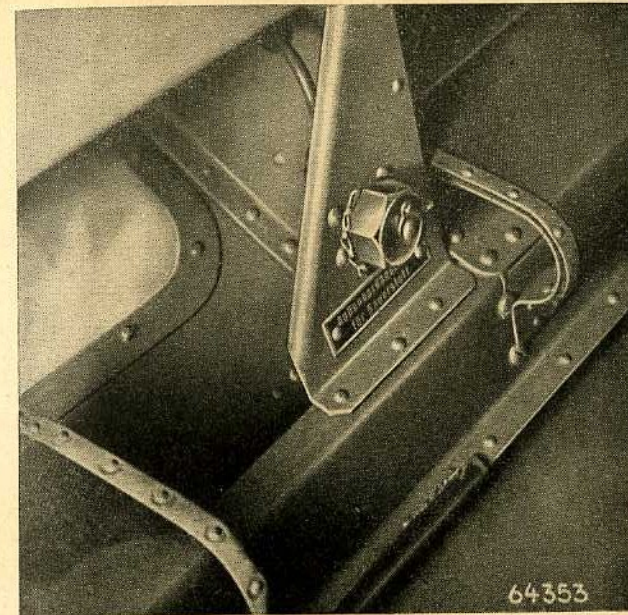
Flaschenfernventil (alte Ausführung)
